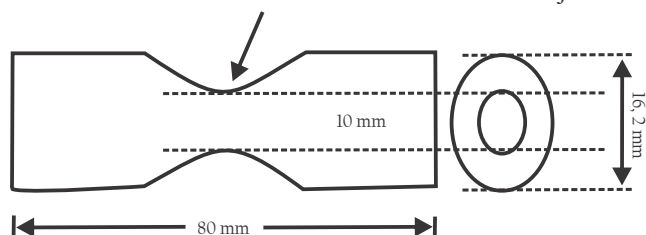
Geometría y dimensiones de probetas ensayadas en corrosión fatiga.
